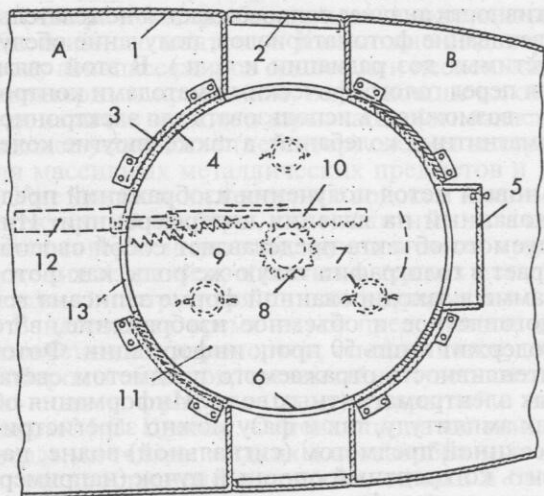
Место размещения капсулы-ловушки (вид сверху) А — пассажирский салон или грузовой отсек; В — кабина экипажа: 1 — фюзеляж; 2 — входная дверь; 3 и 4 — неподвижная и подвижная стенки; 5 — дверь в кабину экипажа; 6 — кольцо; 7 — стойка; 8 — шестерня; 9 — пружина; 10 — зубчатая рейка; 11 — пол капсулы; 12 — гидроусилитель (бустер); 13 — дверь
